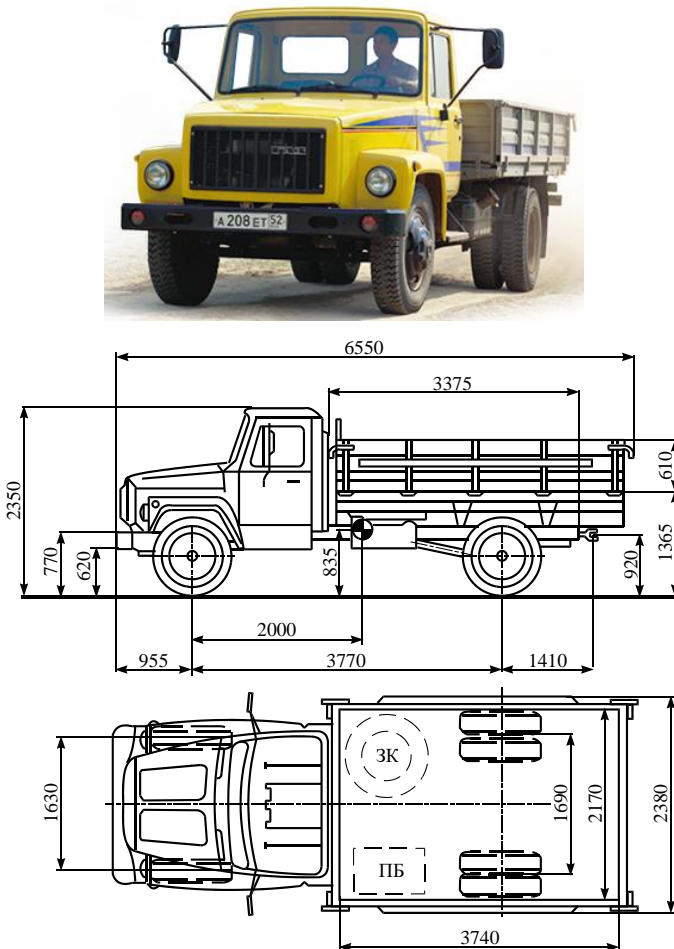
Вантажний бортовий автомобіль ГАЗ-3307 зі стандартною базою (загальний вигляд та габаритні розміри) (Spectekhnika)
